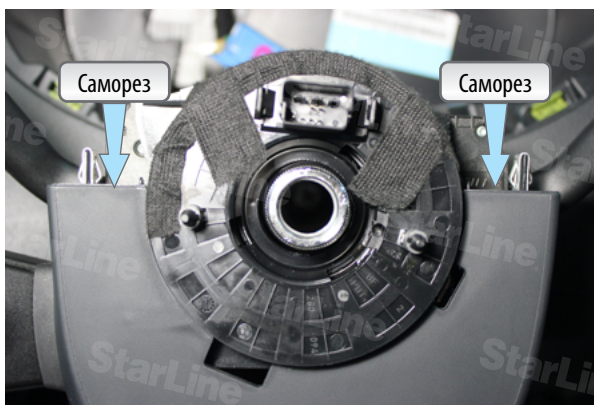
Рулевое колесо снято; саморезы кожуха
